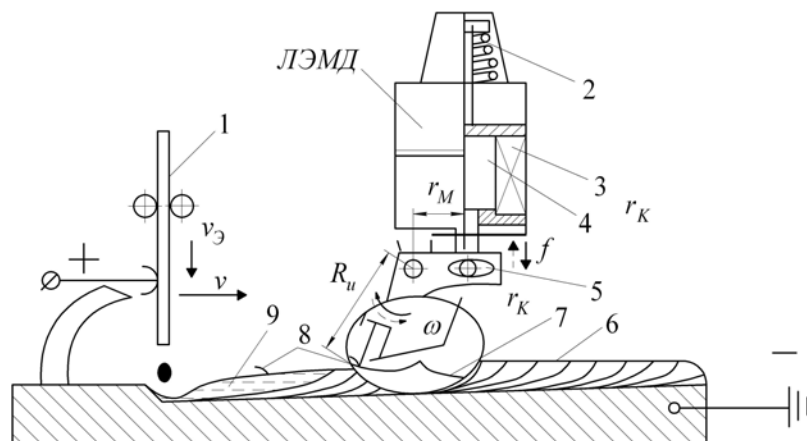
Схема обработки по принципу циклического терморезания с приводом от ЛЭМД: 1 – электрод; 2 – пружина возврата якоря; 3 – обмотка; 4 – якорь; 5 – резец; 6 – обработанная поверхность; 7 – поверхность резания; 8 – стружка; 9 – сварочная ванна; $v_э$, $v_н$ – скорость подачи электрода и наплавки, соответственно; f , ω – усилие и частота возвратно-поступательно-качательного движения; $r_к$ – радиус кривизны
